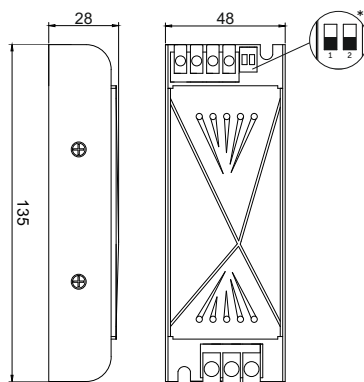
б. Габаритные размеры блока питания Baulamp BL-24V100W IP50
